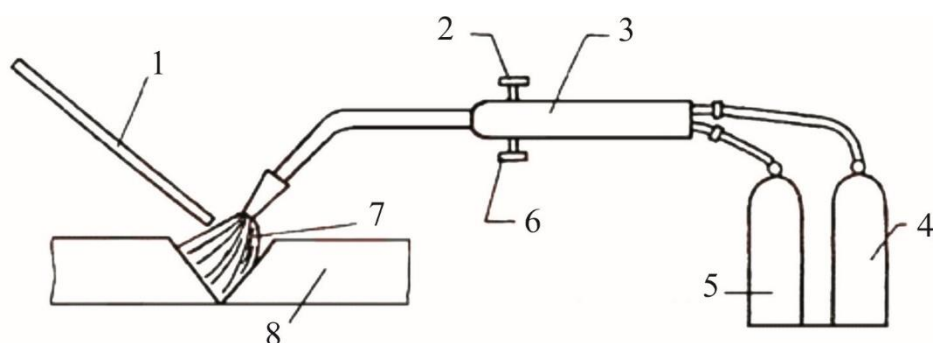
Схема процесса газовой сварки: 1 – присадочный пруток; 2 – вентиль для кислорода; 3 – сварочная горелка; 4 – баллон с кислородом; 5 – баллон с горючим газом; 6 – вентиль для горючего газа; 7 – пламя; 8 – свариваемое изделие
